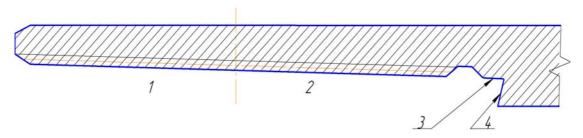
Участки контроля поверхности резьбовых, уплотнительных и упорных поверхностей труб и муфт с резьбовым соединением «ТМК GF»
